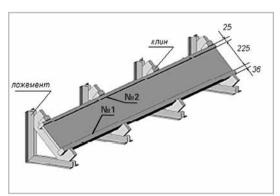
Вид типового сварочного кондуктора для сборки и сварки двутавровых балок
